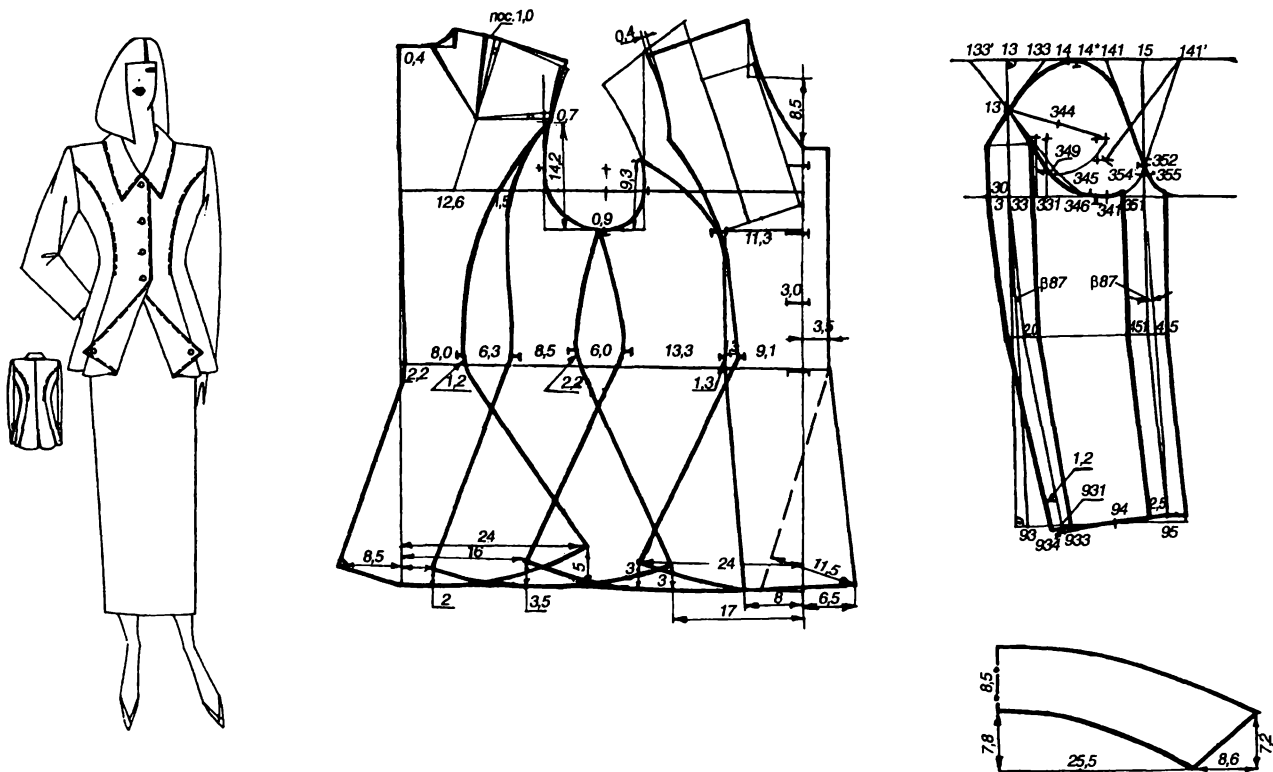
Модель и чертеж конструкции жакета женского полуприлегающего силуэта
